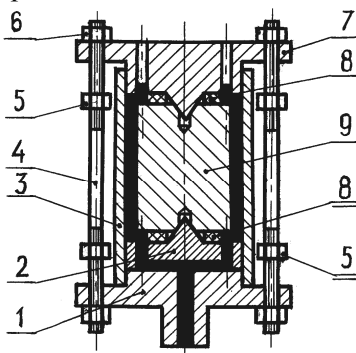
Схема приспособления для нанесения покрытия на образцы
